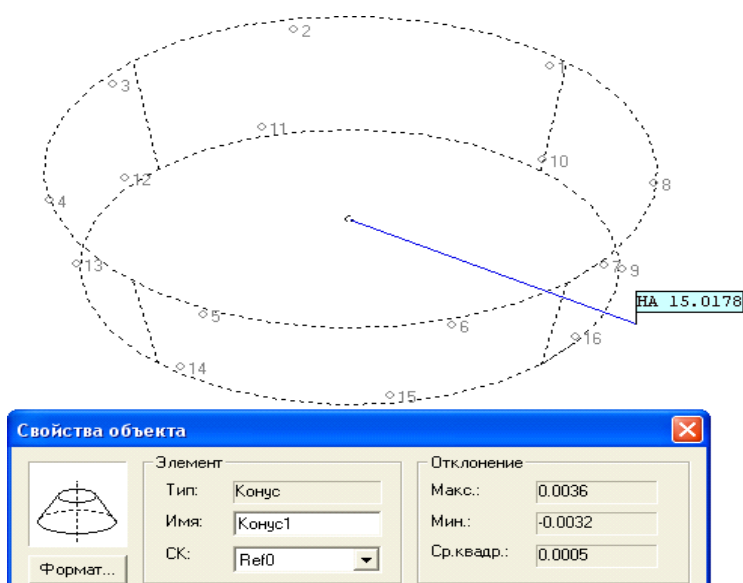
Контроль бігової доріжки кільця конічного підшипника
